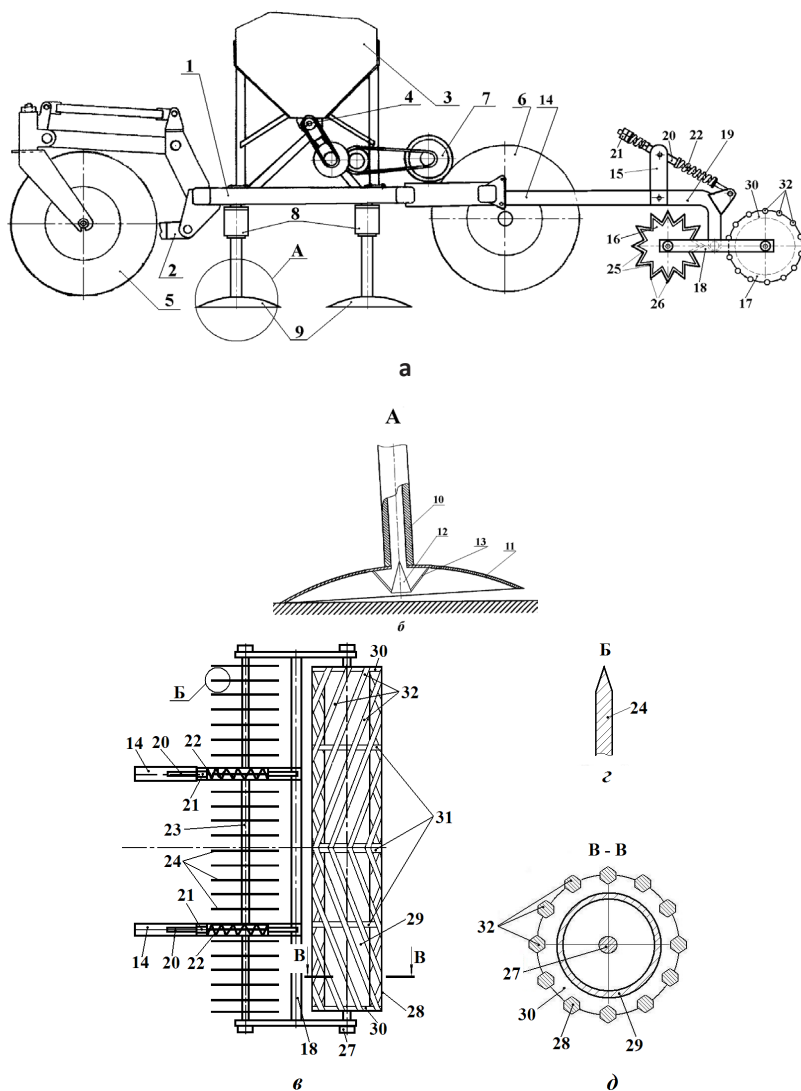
Комбинированный посевной агрегат: а - вид сбоку; б – сошник, вид А; в – катковая приставка, вид сверху; г – поперечное сечение заточенной вершины дискового рыхлителя, вид Б; д – поперечное сечение катка выравнивающего типа по линии В-В
